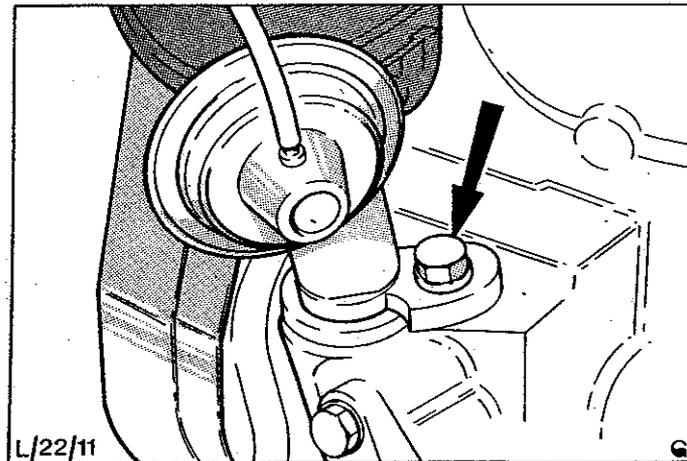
Verteilerklemmschraube beim OHC-Motor.
